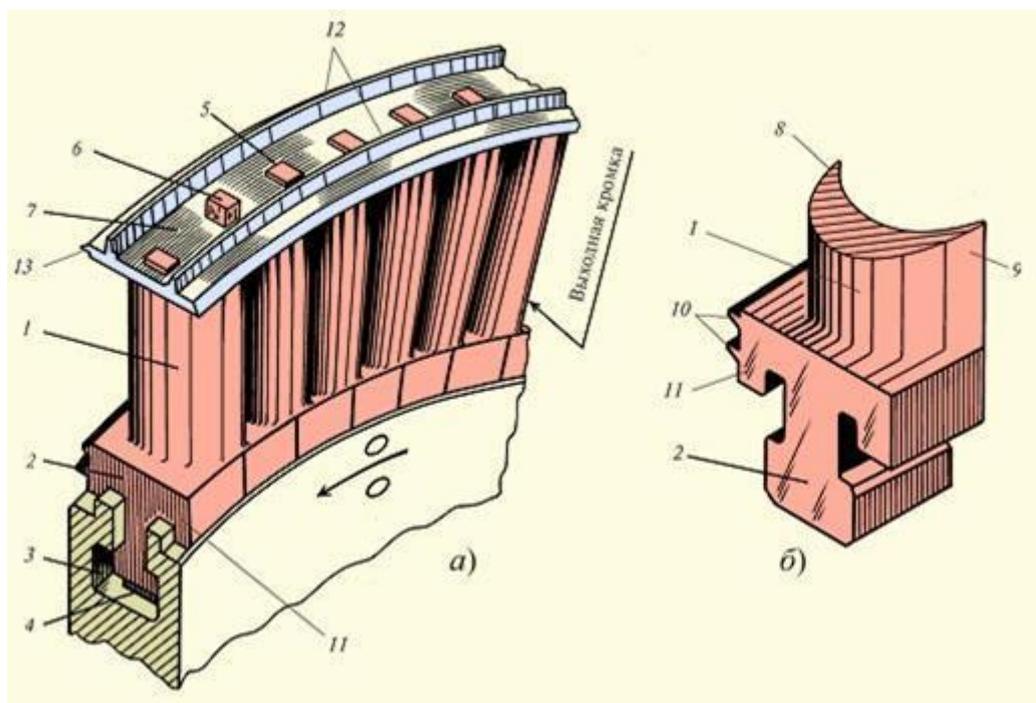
Рабочая лопатка ЦВД и ЦСД
